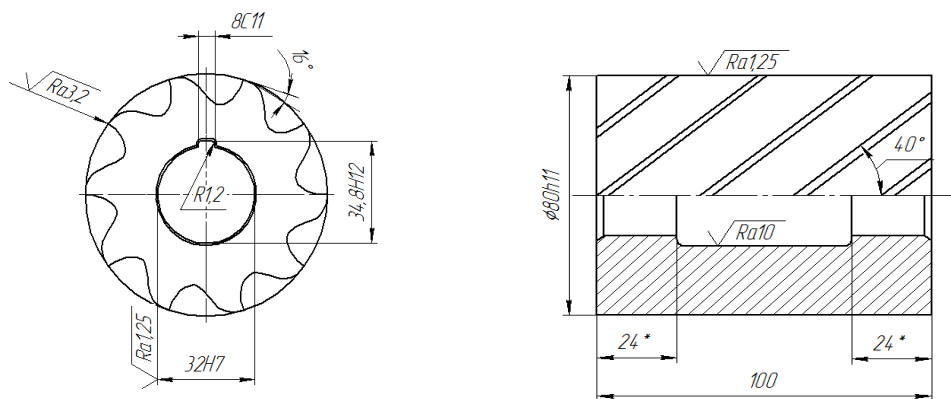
Фреза цилиндрическая (ГОСТ 29092-91)
